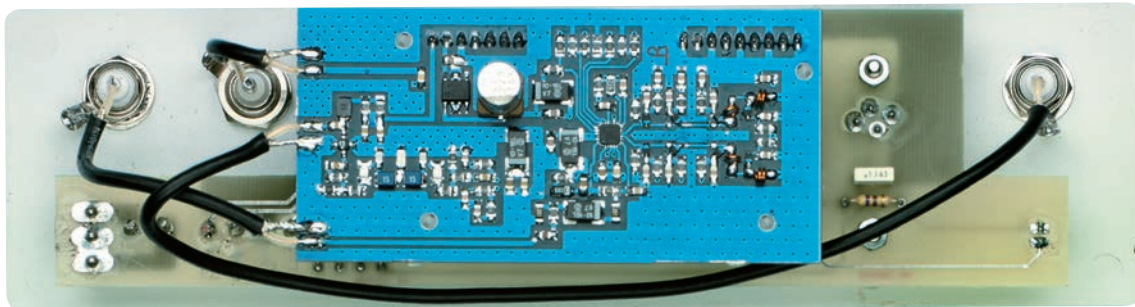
Photo de la face avant avec dessus, déjà fixés, les deux platines. Quand vous relierez les petits câbles coaxiaux à la platine CMS, souvenez-vous que la tresse de blindage de chaque câble coaxial est à souder sur la piste de Masse.
